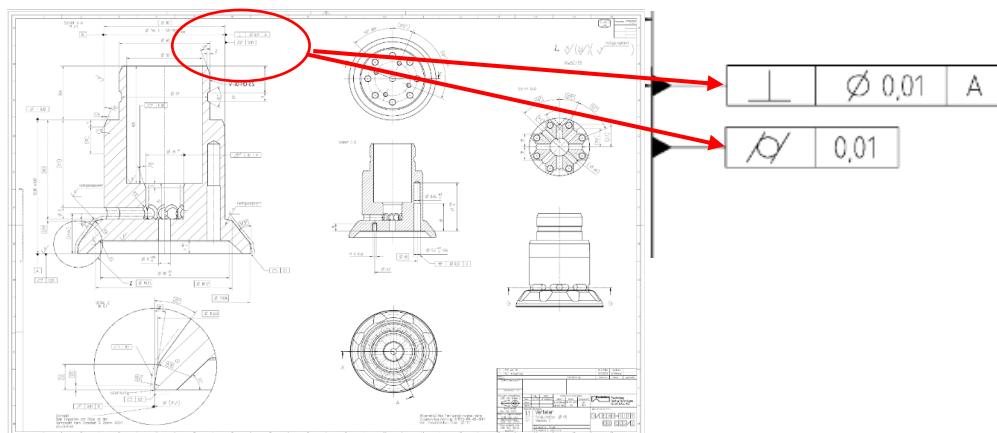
Výkresová dokumentace jádra, detail měřených hodnot geometrických tolerancí
